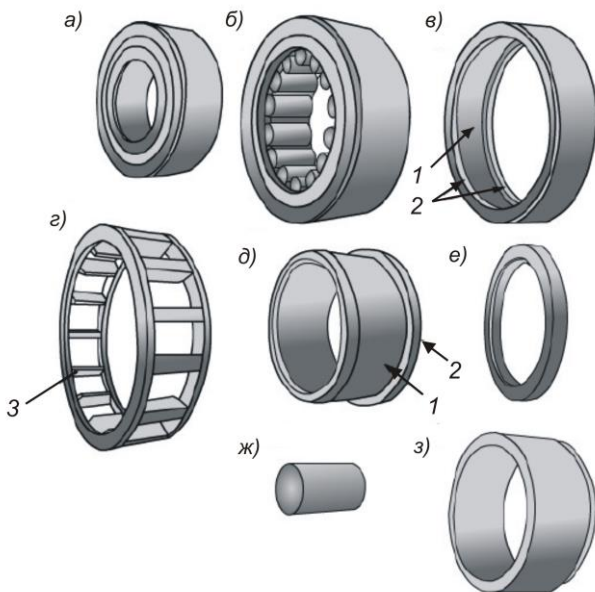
Роликовый цилиндрический подшипник:
